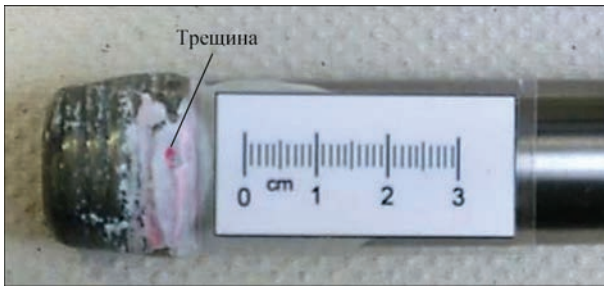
Трещина в кратере (104) замыкающего валика наплавленного слоя, выполненного дуговой наплавкой порошковой проволокой в инертном газе (процесс 132, наплавленный металл группы Co2 [4–6])
